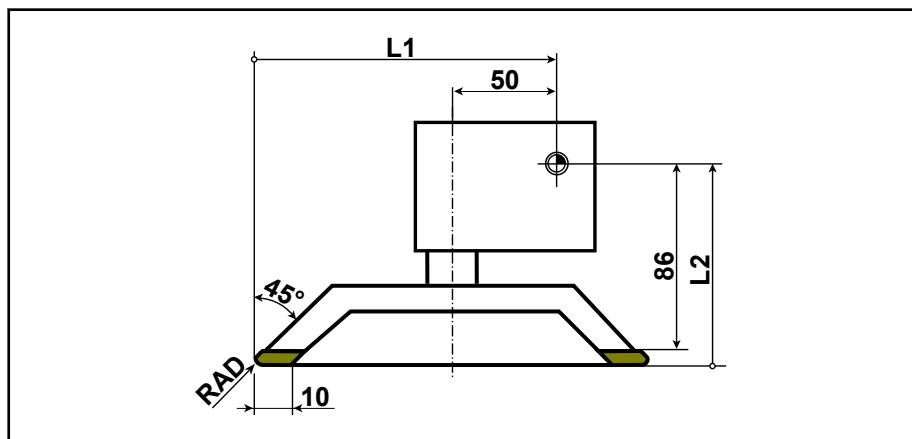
Beispiel Werkzeugbeschreibung für eine Topfscheibe
